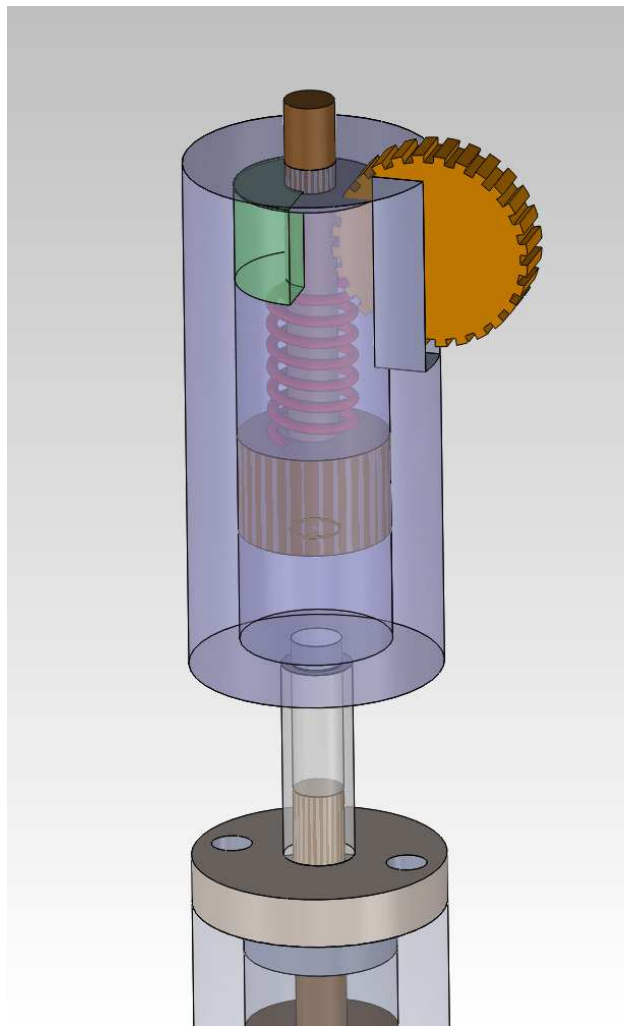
Attuatore pneumatico per la movimentazione del corpo molitore.
